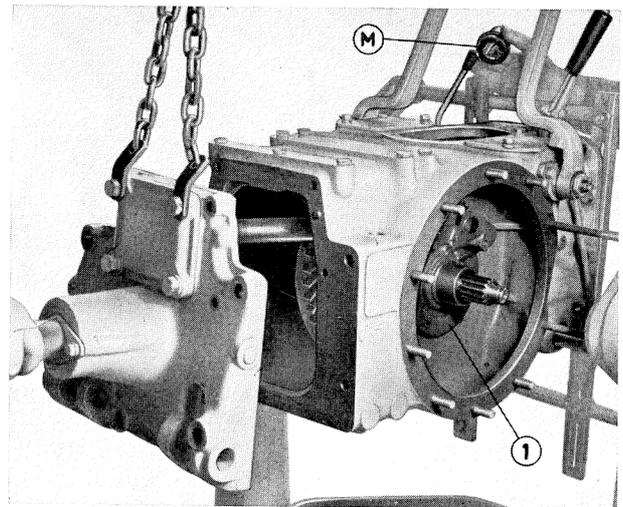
Dépose du couvercle arrière du carter de transmission.
